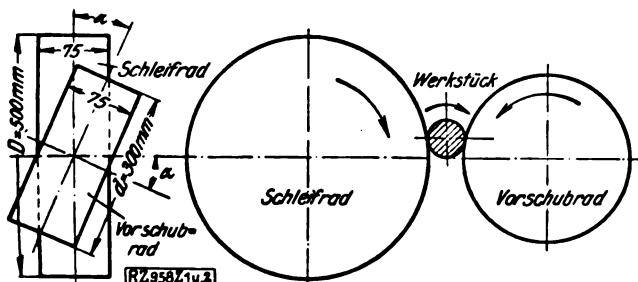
und 9. Werkstückanordnung beim Rundschleifen ohne Aufspannen
